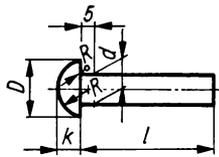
zeigt eine Übersicht der gebräuchlichsten Niete, wie sie im Maschinenbau, Kesselbau und Stahlbau verwendet werden.
